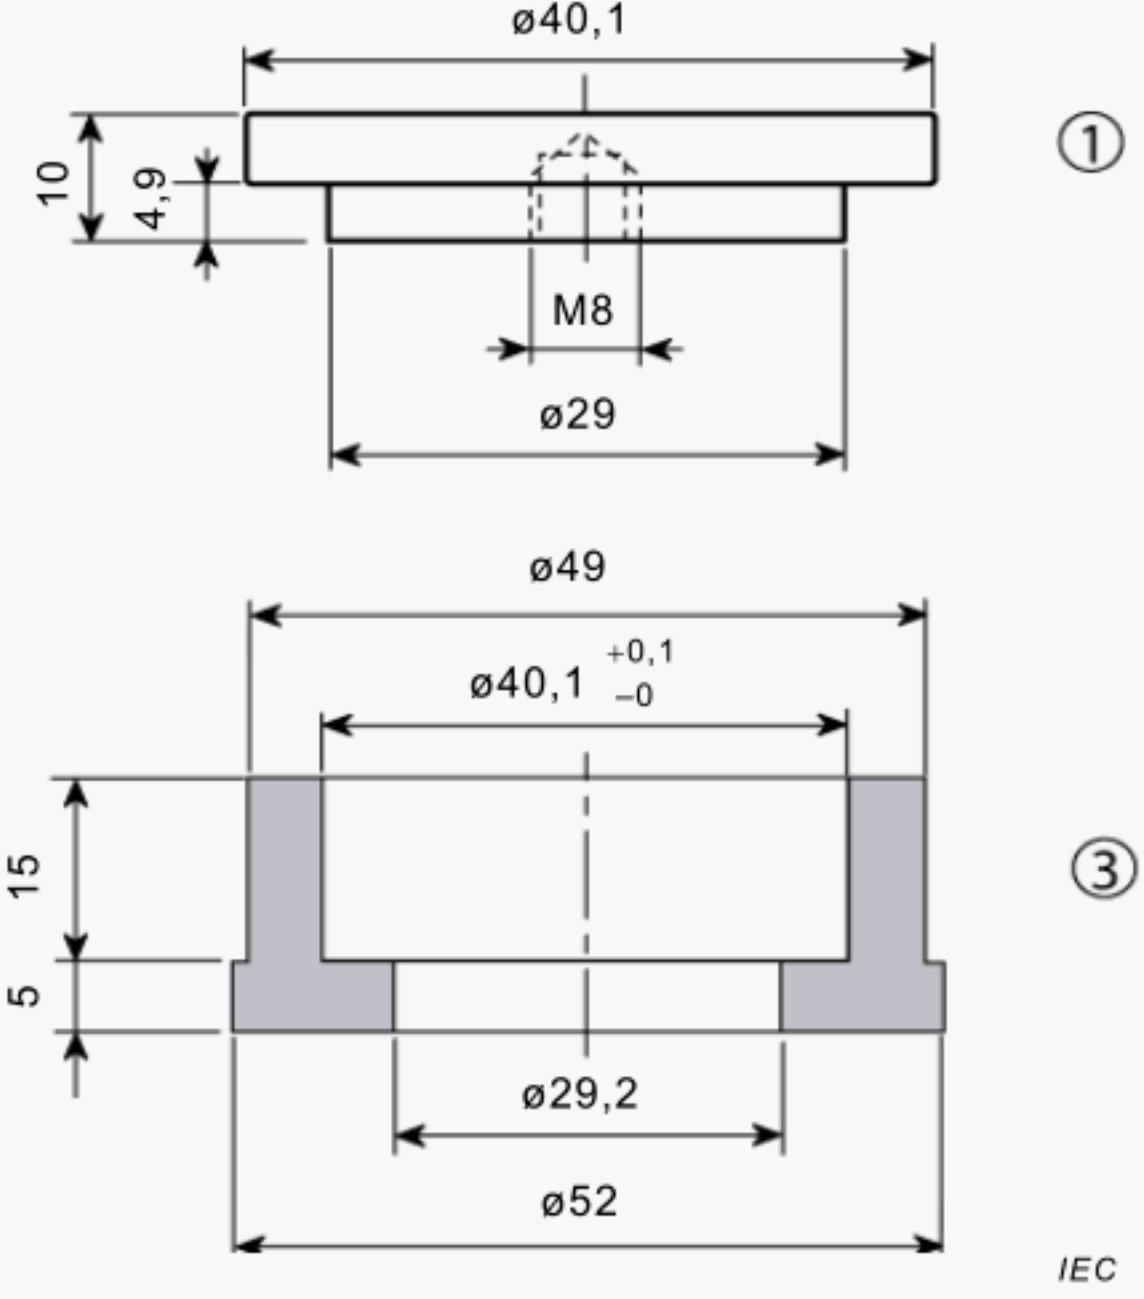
Pour tube rempli de mousse de 39 mm de diamètre
